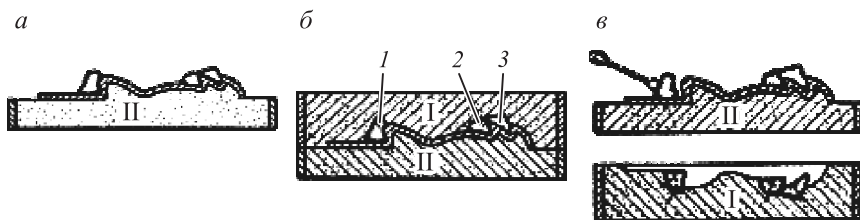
Технология ручного изготовления формы для отливки барельефа: а – изготовление кусков по модели; б – изготовление нижней полуформы; в – снятие кусков с модели и укрепление их в форме; 1–3 – куски; I – нижняя полуформа; II – верхняя полуформа
